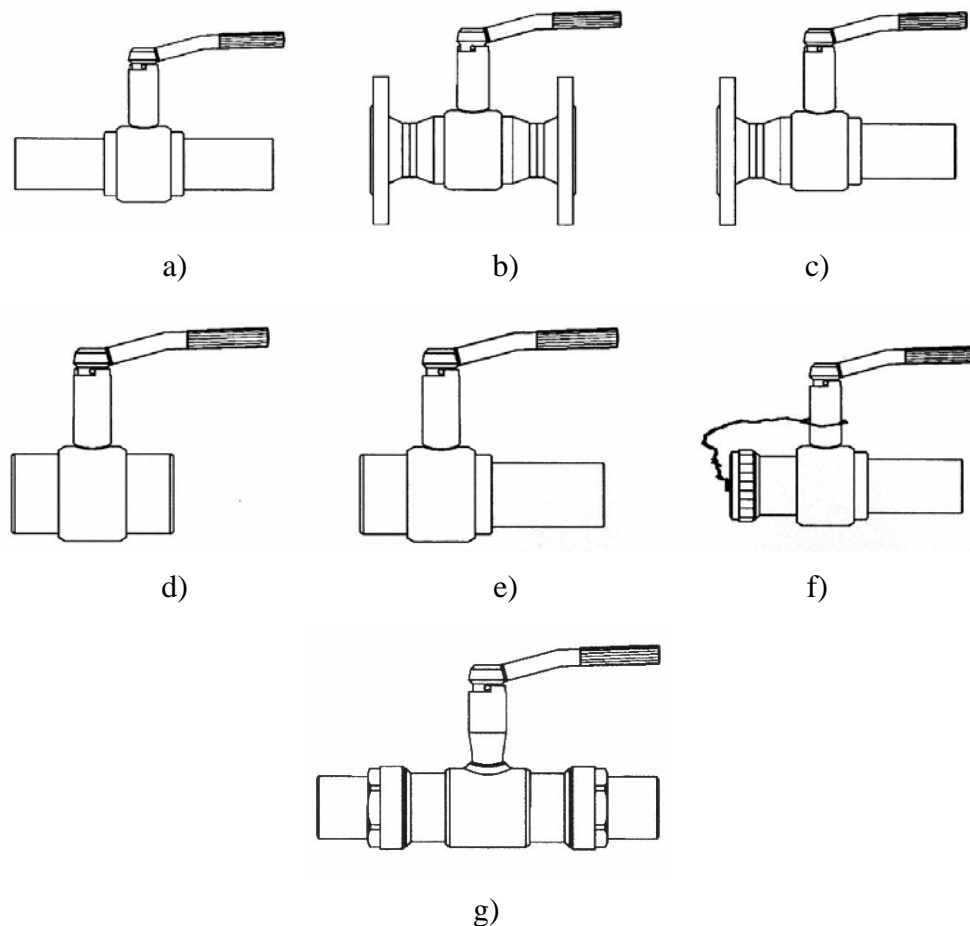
Variante constructive pentru racordarea robinetelor cu bilă
